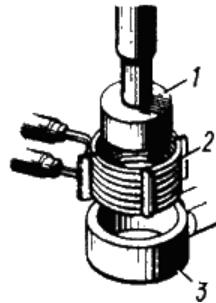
Схема установки для закалки стальных деталей с нагревом ТВЧ .
